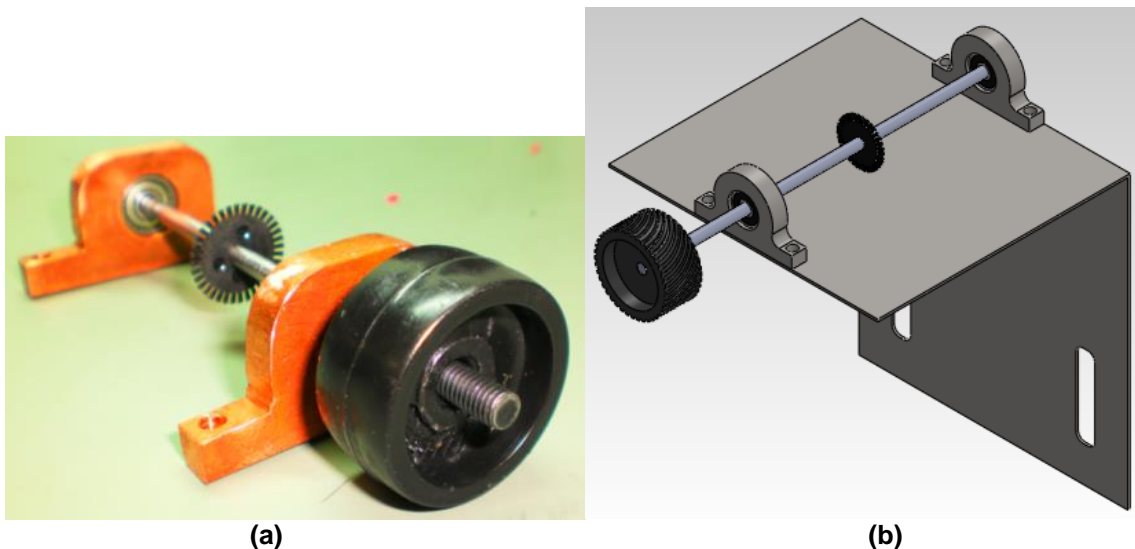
Conjunto da roda dentada do *encoder* da roda traseira
